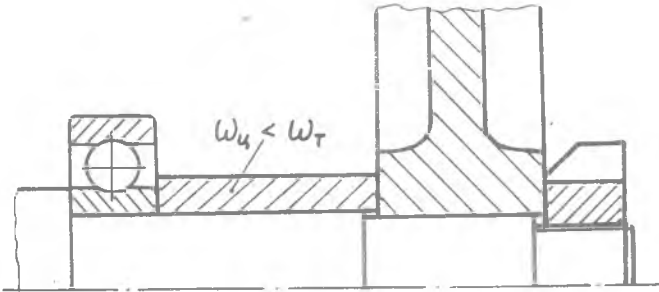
Крепление колеса и подшипника, разделённых втулкой
